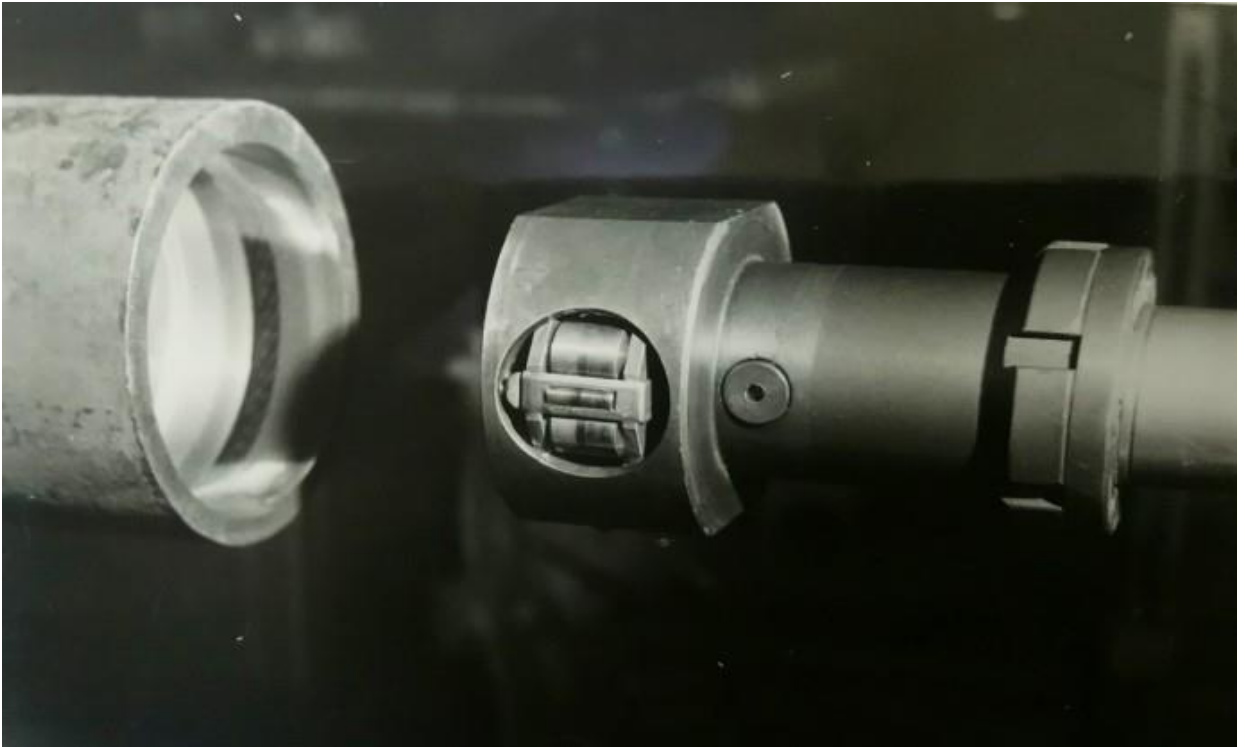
Розкочування внутрішніх поверхонь на токарному верстаті
